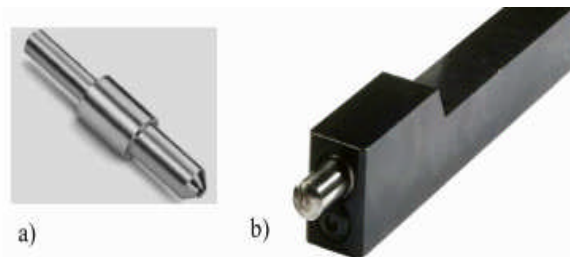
Outil du galetage commercialisé par la firme COGSDILL TOOL:
